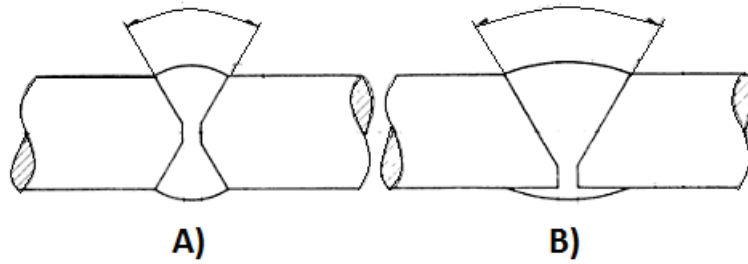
Empalmes por soldadura a tope.
